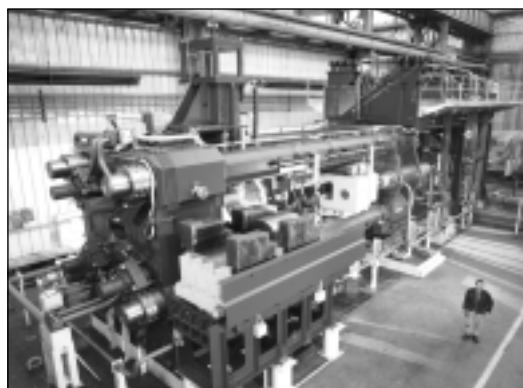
Pressa da estrusione da 6050 tonnellate. (foto Metra)
